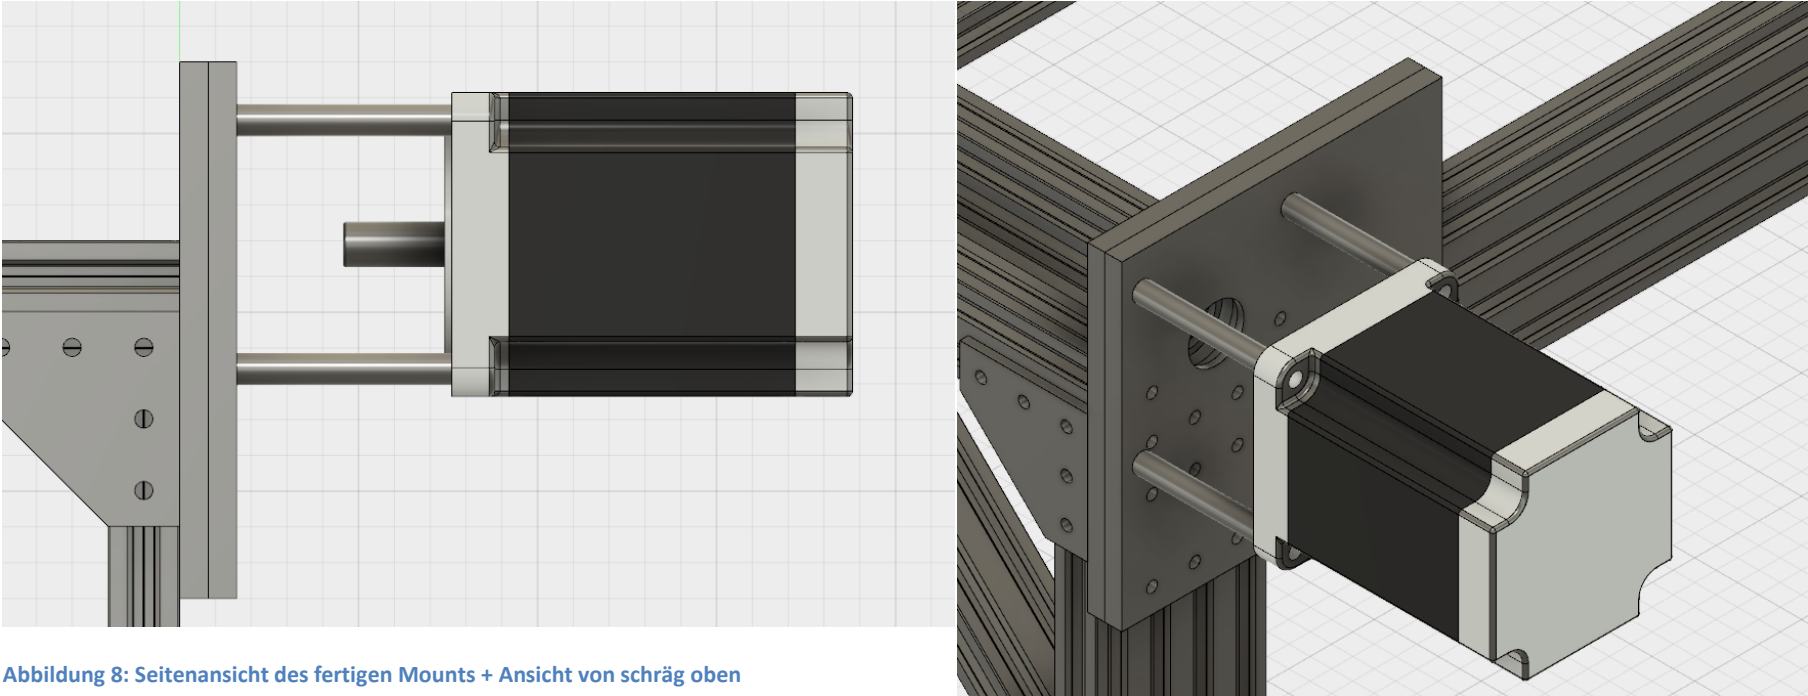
Seitenansicht des fertigen Mounts + Ansicht von schräg oben
